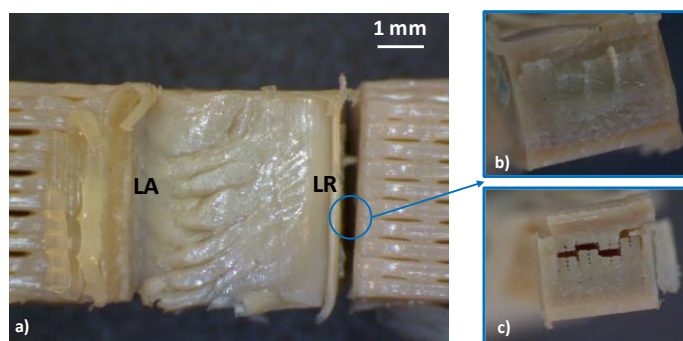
Macrografia do provete após Ensaio 2: a) Superfície superior do provete, b) Superfície de fratura do cordão de soldadura do LR, c) Superfície de fratura da interface do material base com o LR.
